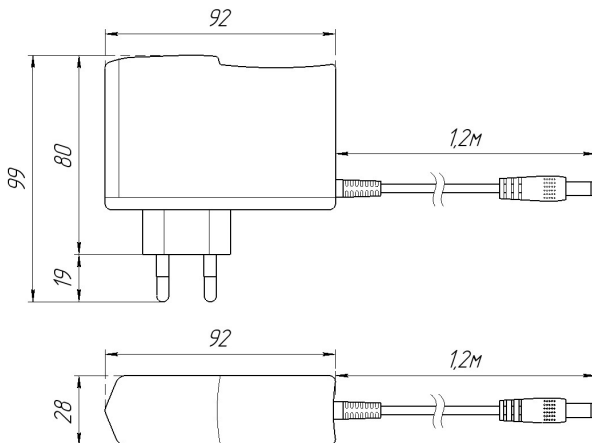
Габаритные размеры блока питания Geniled GL-12V12WP20 Plug и GL-12V30WP20 Plug.
